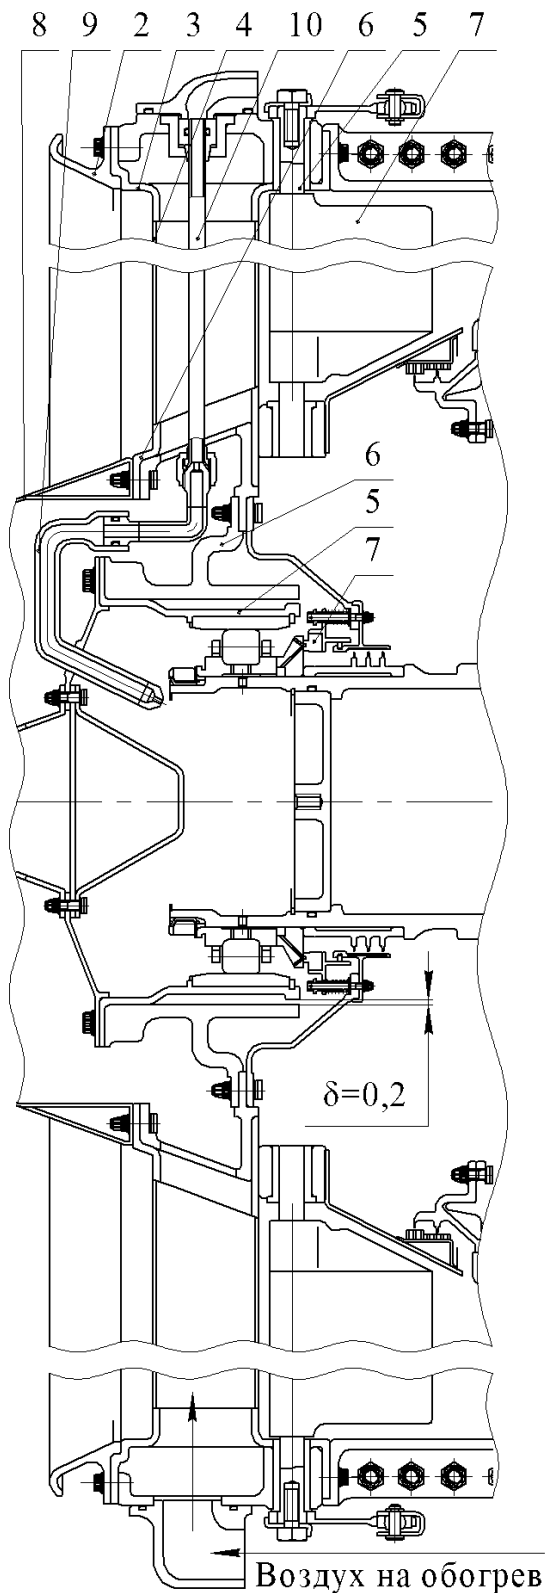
Передняя опора ТРДД F100-PW-229, конструкция и конструктивная схема:
